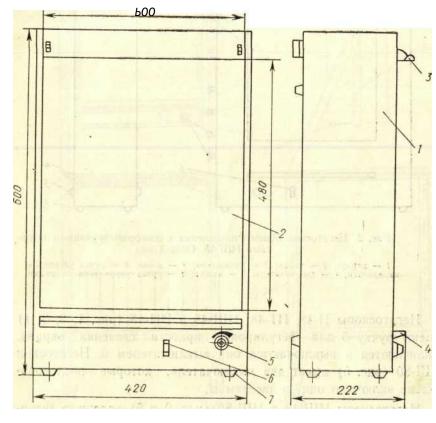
Негатоскоп общего назначения H-48 / — корпус, 2 — экран; 3 — кронштейн; 4 — лоток; 5 — ручка регулировки яркости; 6 — выключатель; 7 — ножка.
